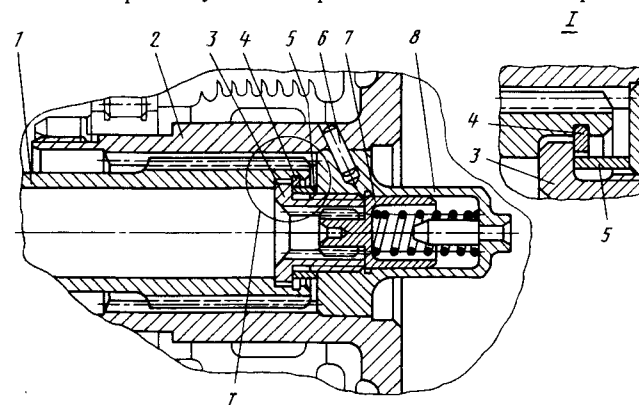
Соединение рессоры редуктора с передней цапфой компрессора в ТВД: 1 — рессора; 2 — передняя цапфа компрессора; 3 — фасонный болт; 4 — пружинящее кольцо; 5 — распорная втулка; 6 — штифт; 7 — фасонный стопор; 8 — заглушка
